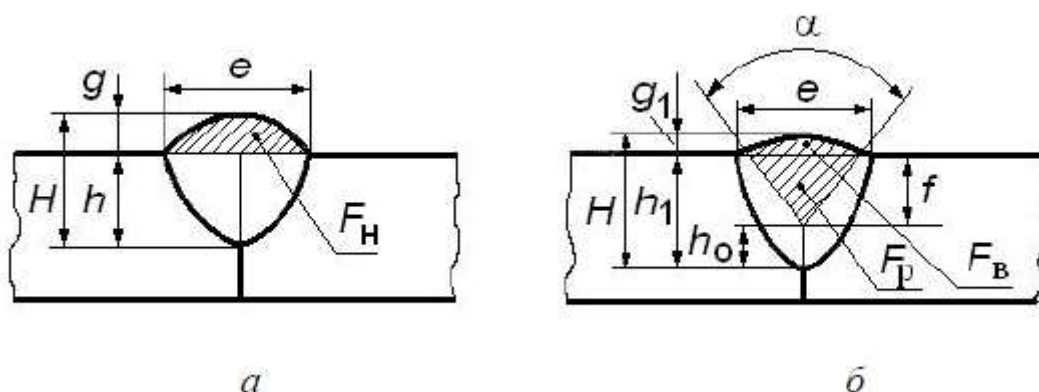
Размеры швов, выполненных на одном режиме при сварке без зазора и разделки (а) и при сварке в разделку (б)
